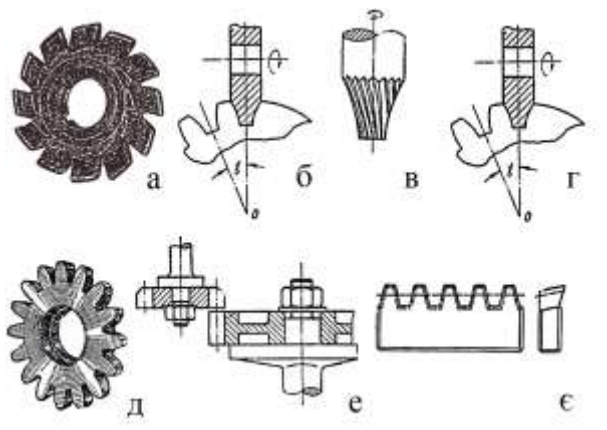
Способи виготовлення зубів зубчастих передач [9]
